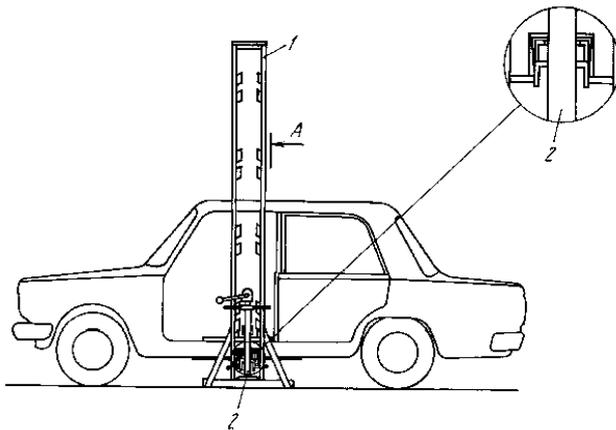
Опрокидыватель. Вид сбоку.
